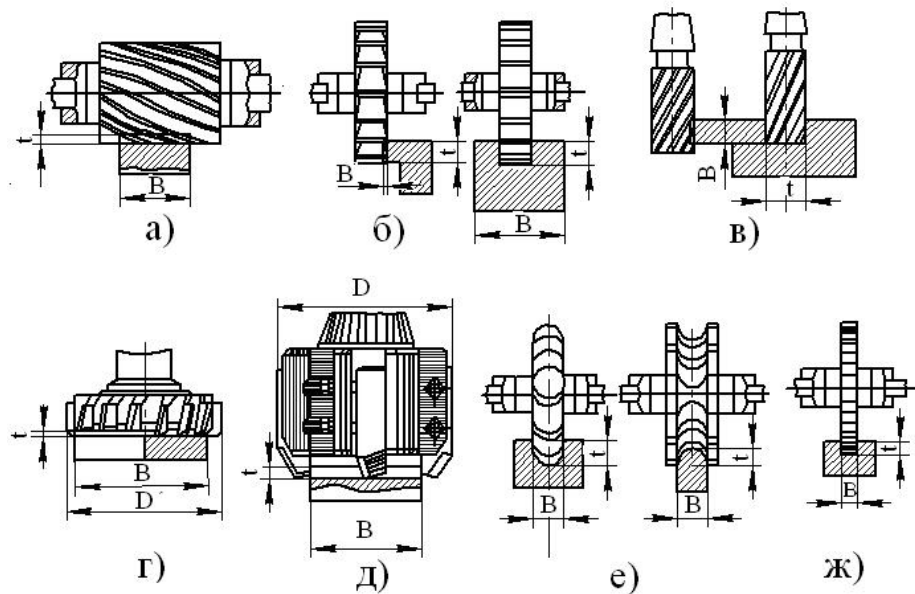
Схеми визначення глибини різання залежно від виду фрезерування
